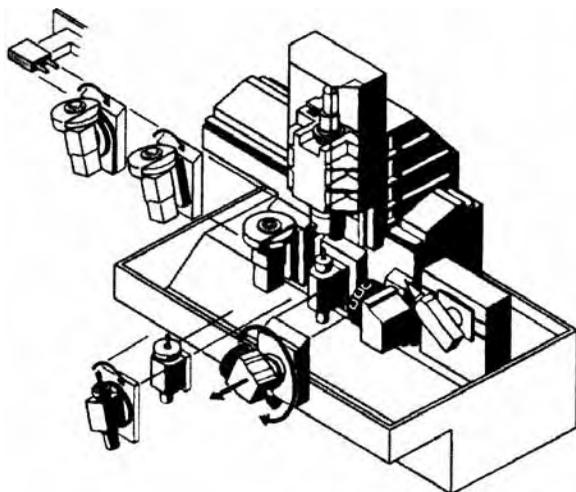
Токарно-шлифовальный многоцелевой станок модульной конструкции фирмы Index-Werke GmbH&Co.KG
